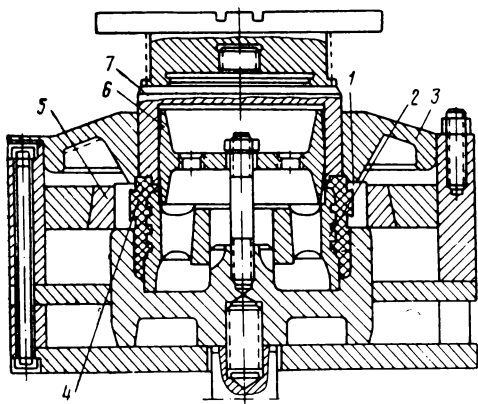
Прессформа для изготовления коллекторов с изоляцией из пластмассы:
